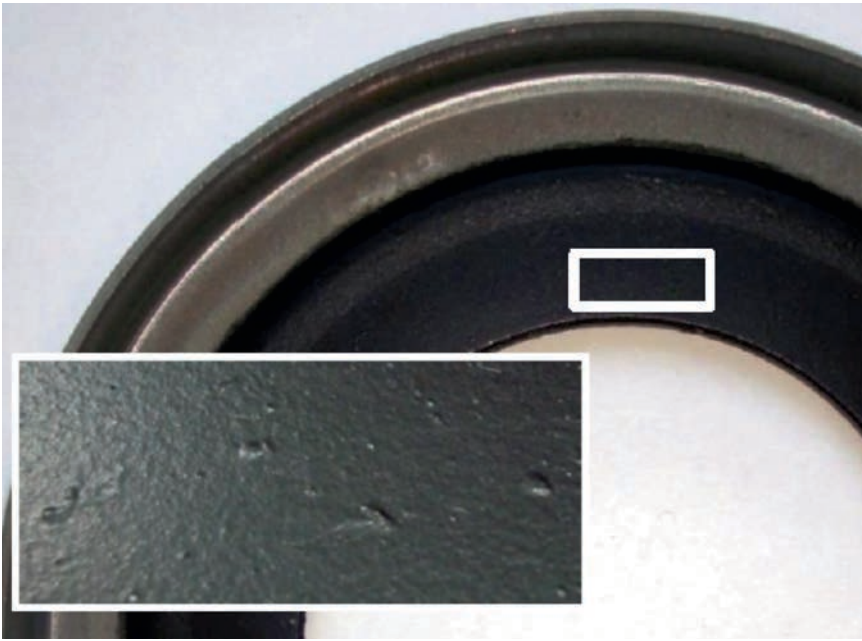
> Raue Oberflächen der Haftmittelschicht führen zu hoher Streuung bei kontaktierender Messung.
